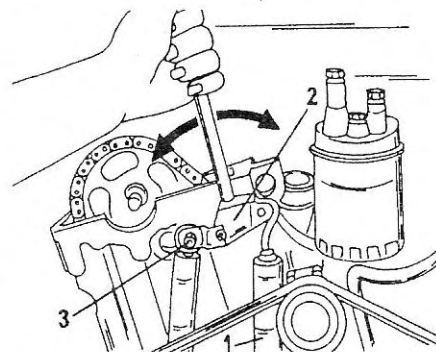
Разгрузка натяжного устройства плоского ремня привода агрегатов.
